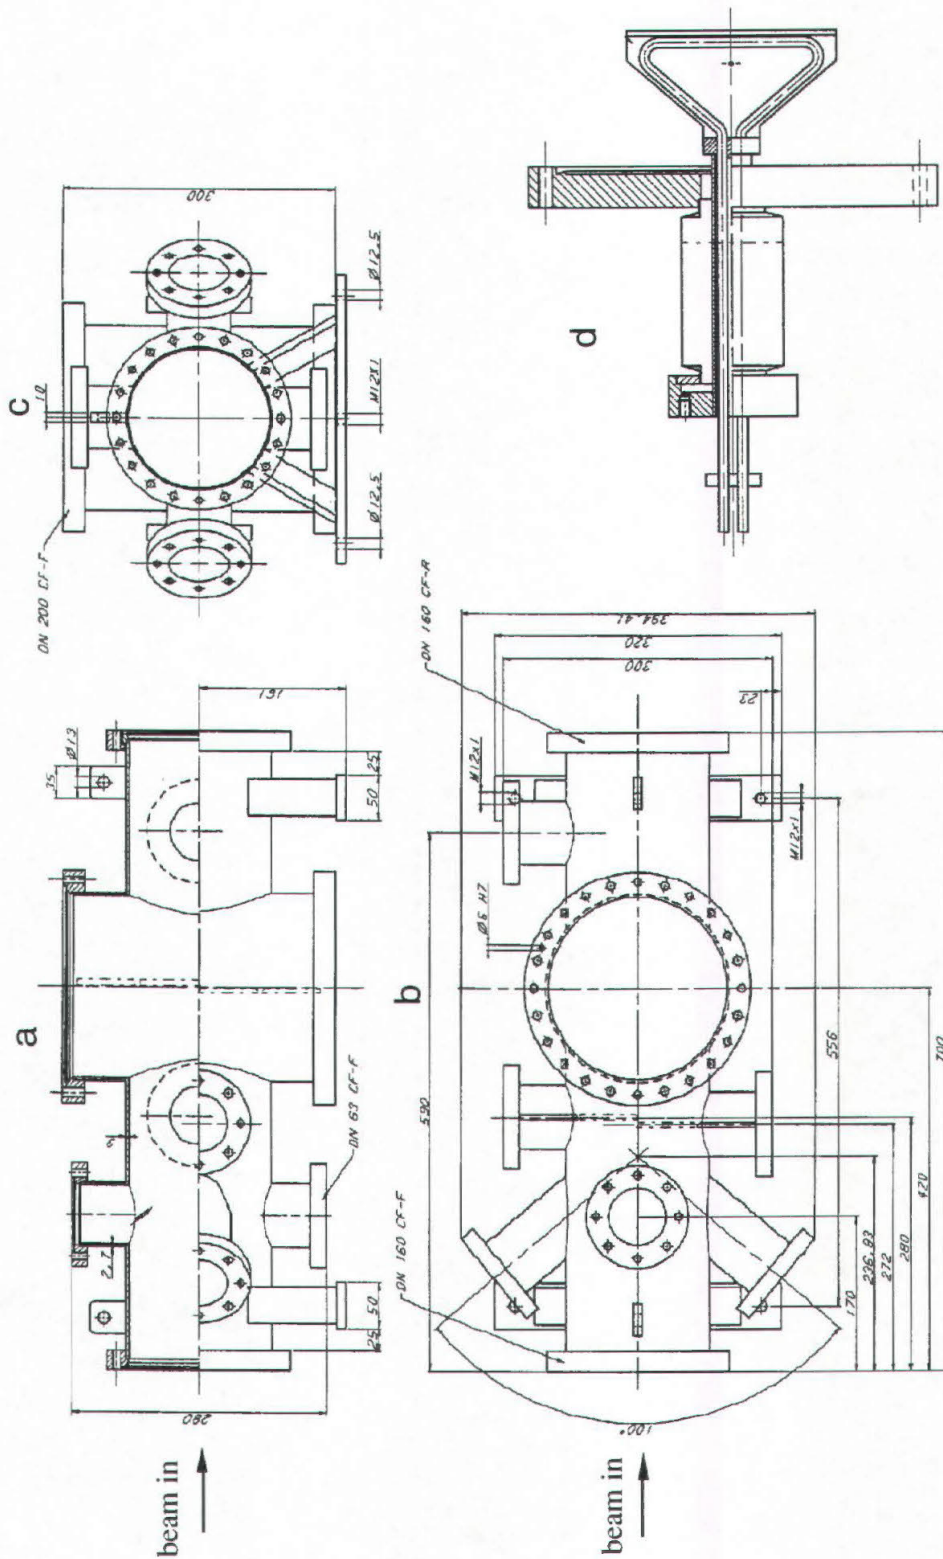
Prospetto (a), pianta (b), vista frontale (c) della camera delle slit. Vista laterale di una slit orizzontale, montata su una flangia. È visibile la canalizzazione interna. Le figure non sono in scala.
